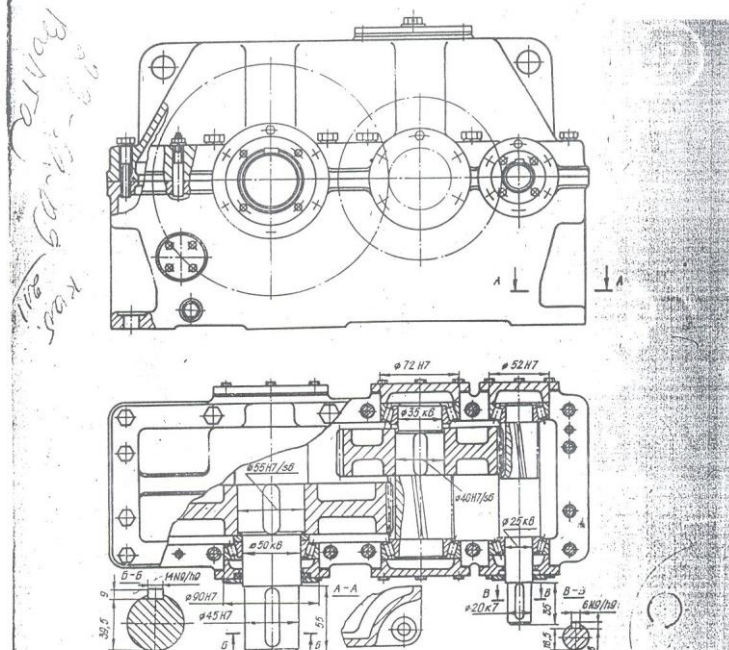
Двухступенчатый цилиндрический редуктор
